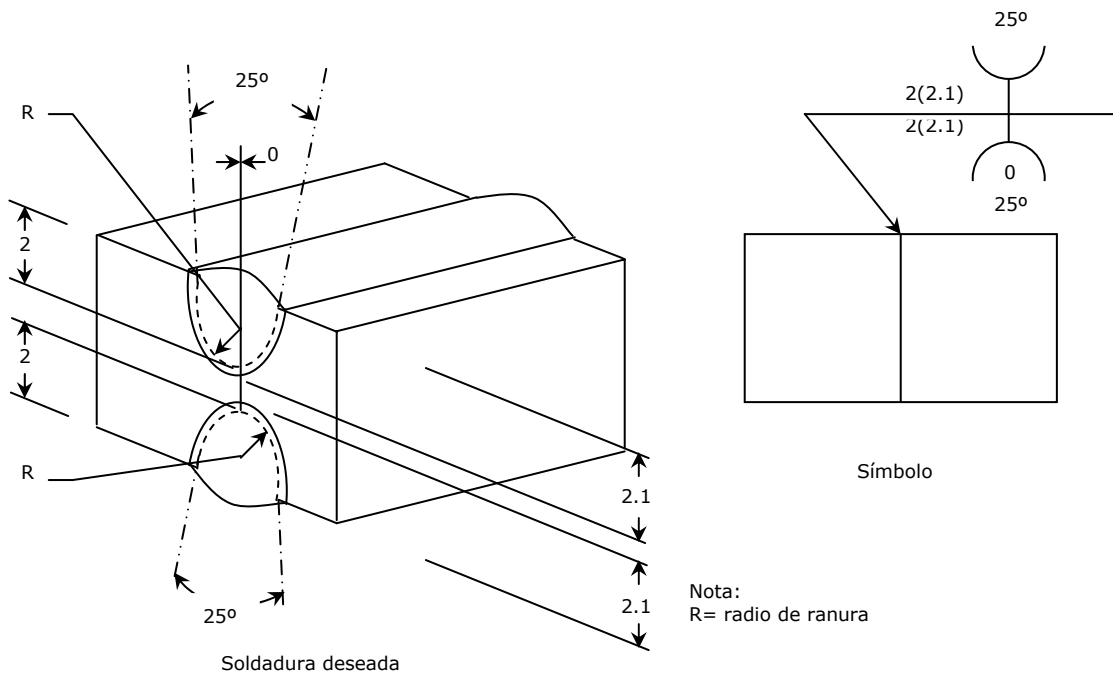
Símbolo de soldadura que aplica para ambos lados de la unión
